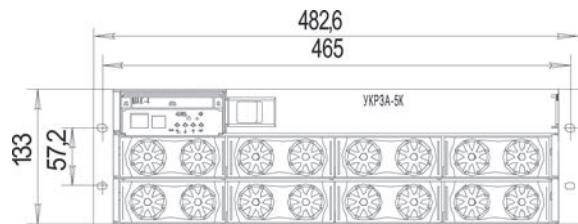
Габаритный чертеж УКРЗА-5К
